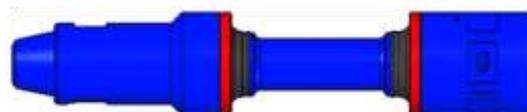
Лепестковый шарнирный карданный вал [34]
